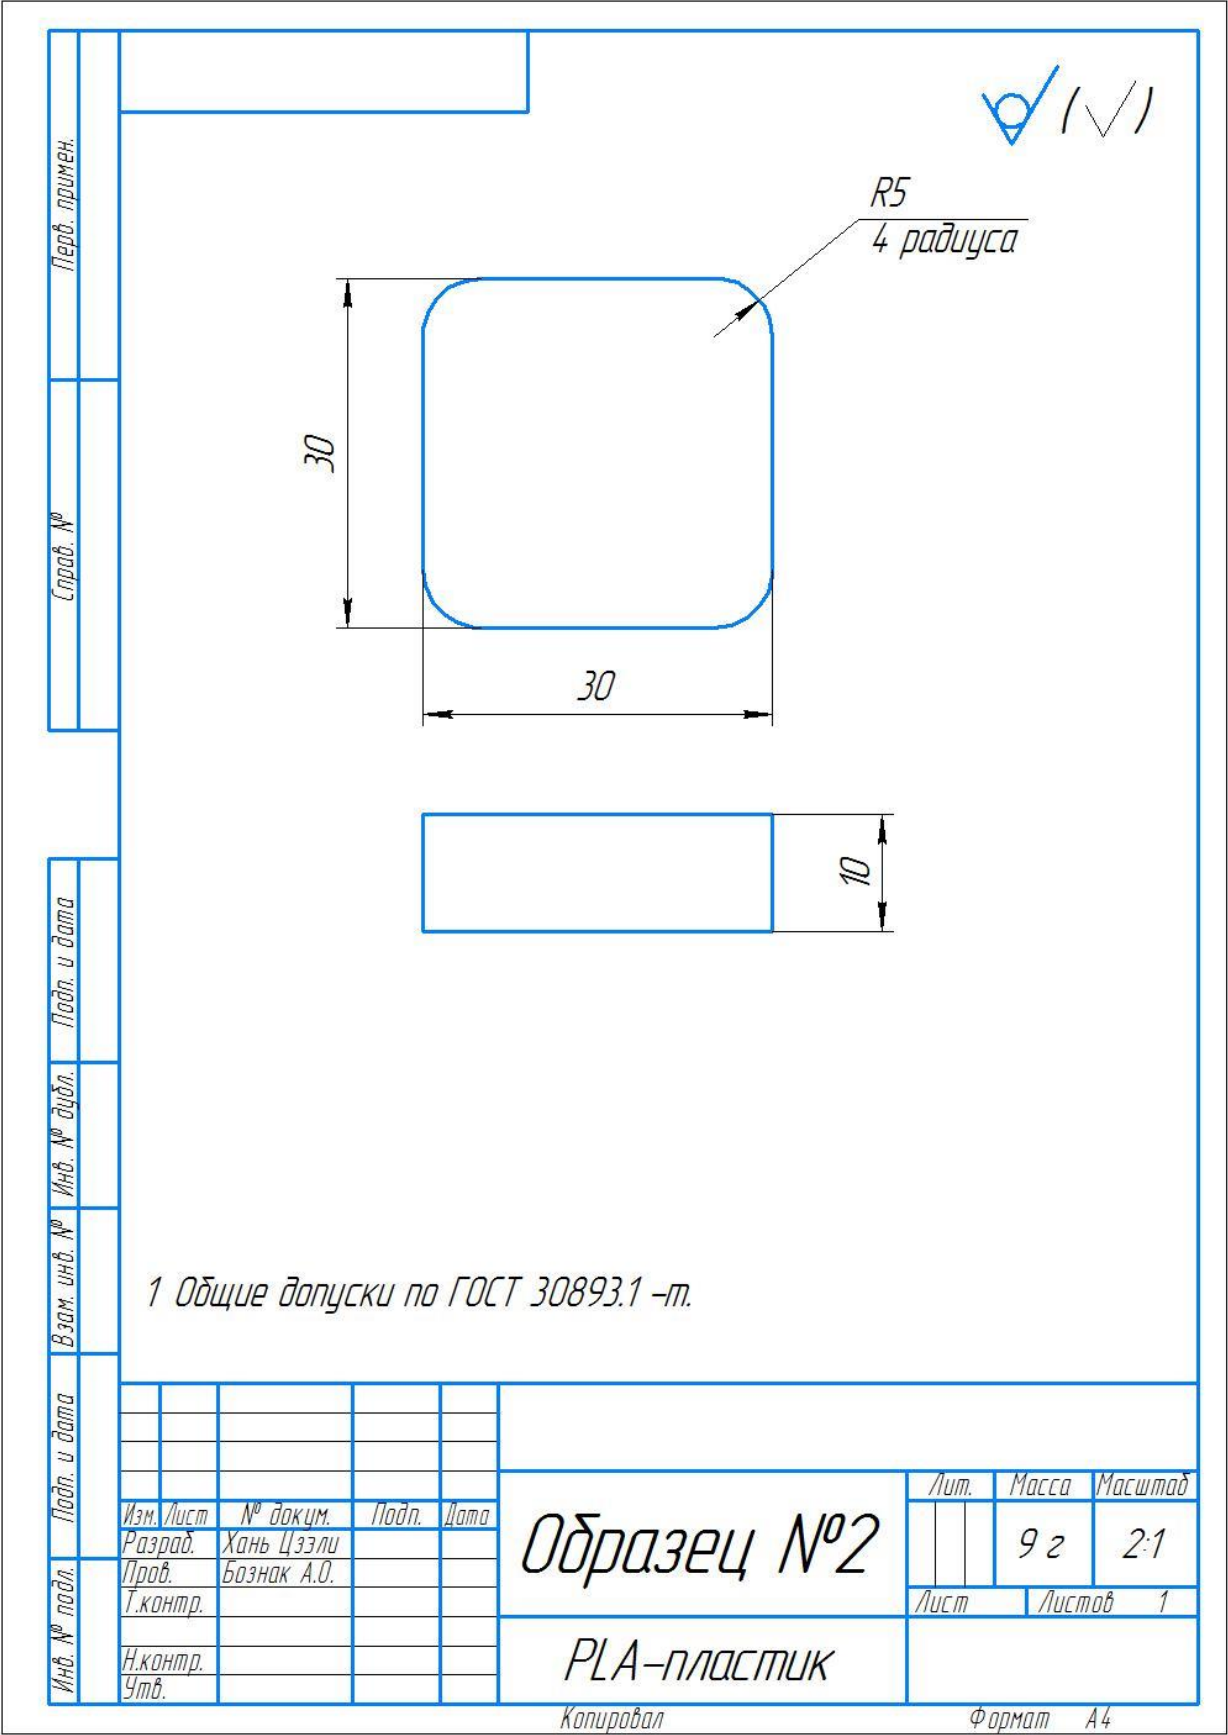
Чертеж детали «Образец №2»
